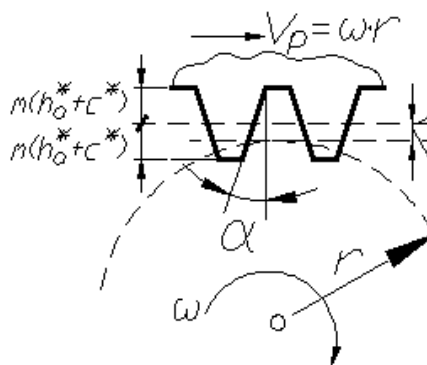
Розміщення зубонарізної рейки і зубчастого колеса (перша штрихова пряма – середня пряма рейки, друга – початкова пряма рейки, штрихова дуга – ділительний діаметр колеса).
